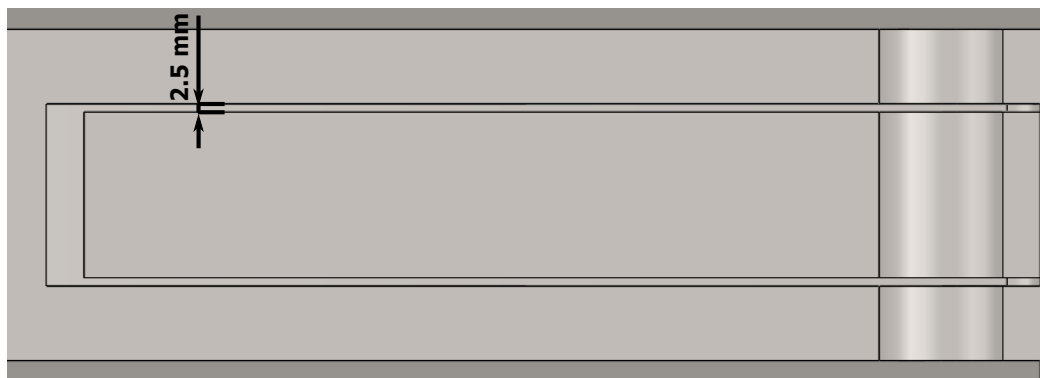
Vista dall'alto incastro versione 2.0 struttura
